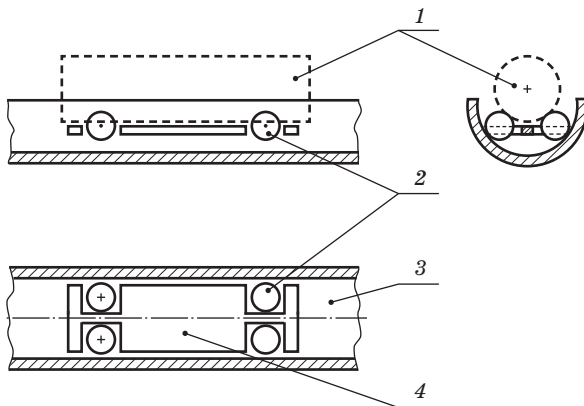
Держатель образца: 1 — образец; 2 — опорные шарики; 3 — опорная трубка; 4 — держатель шариков
